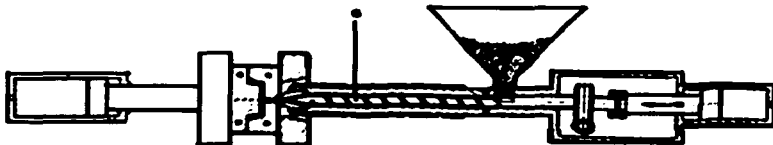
Diagrama simplificado de una máquina de moldeo por inyección con husillo reciprocante. Nótese que el molde está cerrado, mientras que el husillo (6) está al final de la carrera de inyección.
